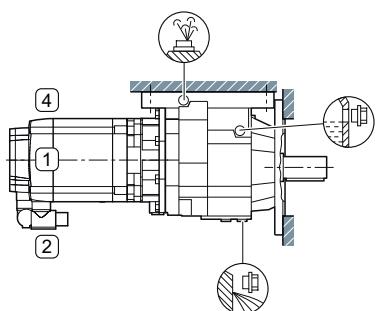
Einbaulagen für Servo-Stirnradgetriebemotoren ZB und DB, Fußausführung, Flanschausführung, Baugrößen 29, 2-stufig und 3-stufig
